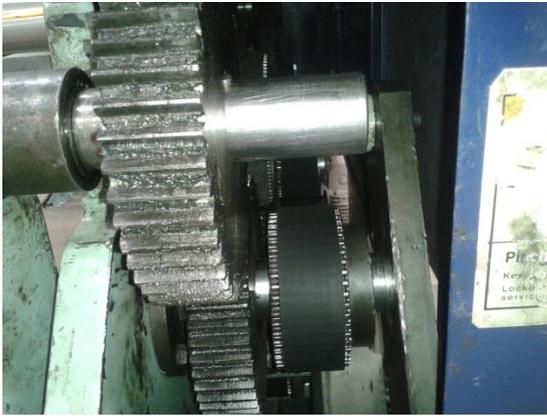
Engranajes dañados de la máquina cortadora de cartón.
